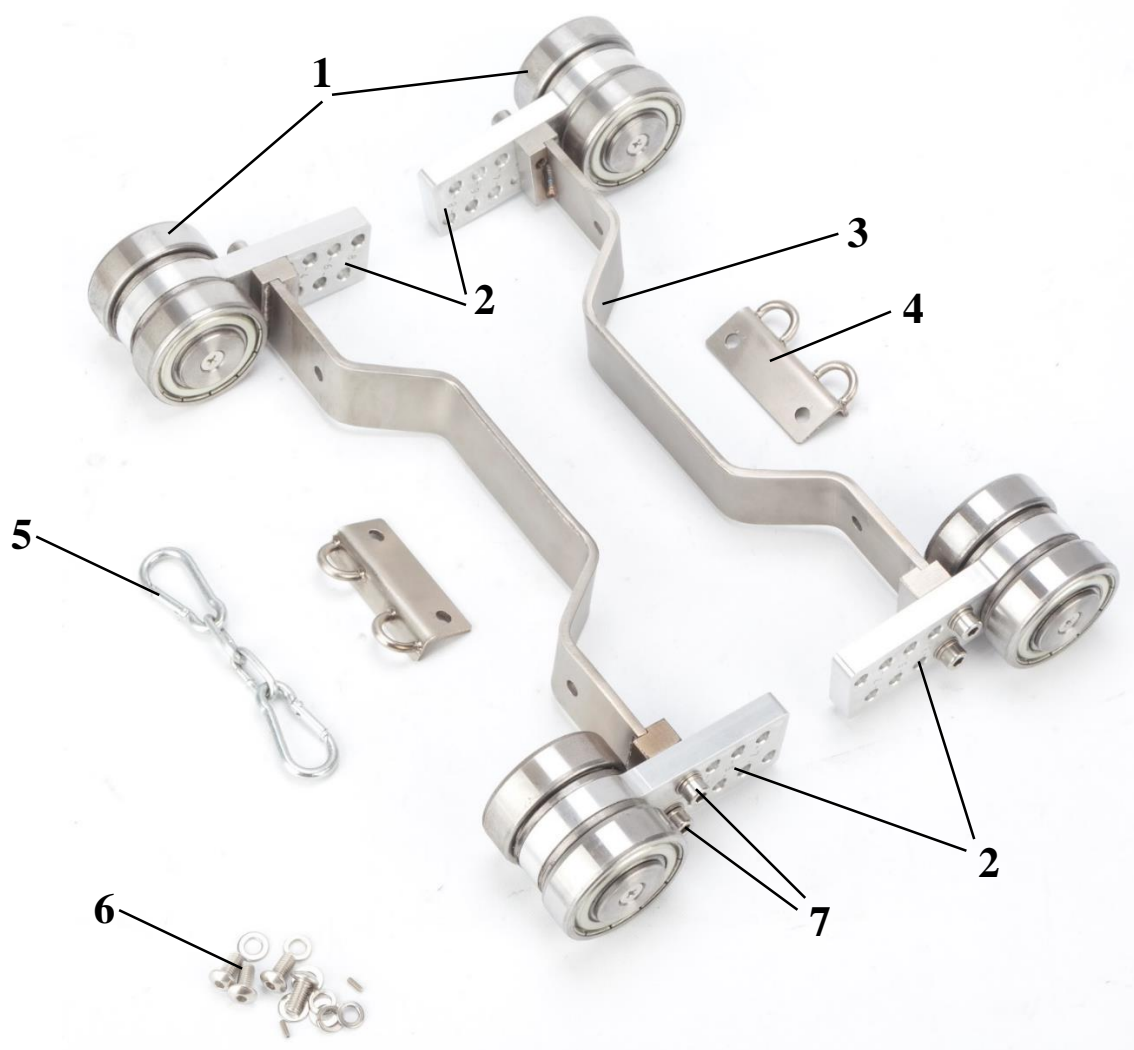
Общий вид магнитных колес ЭКО-10МК
